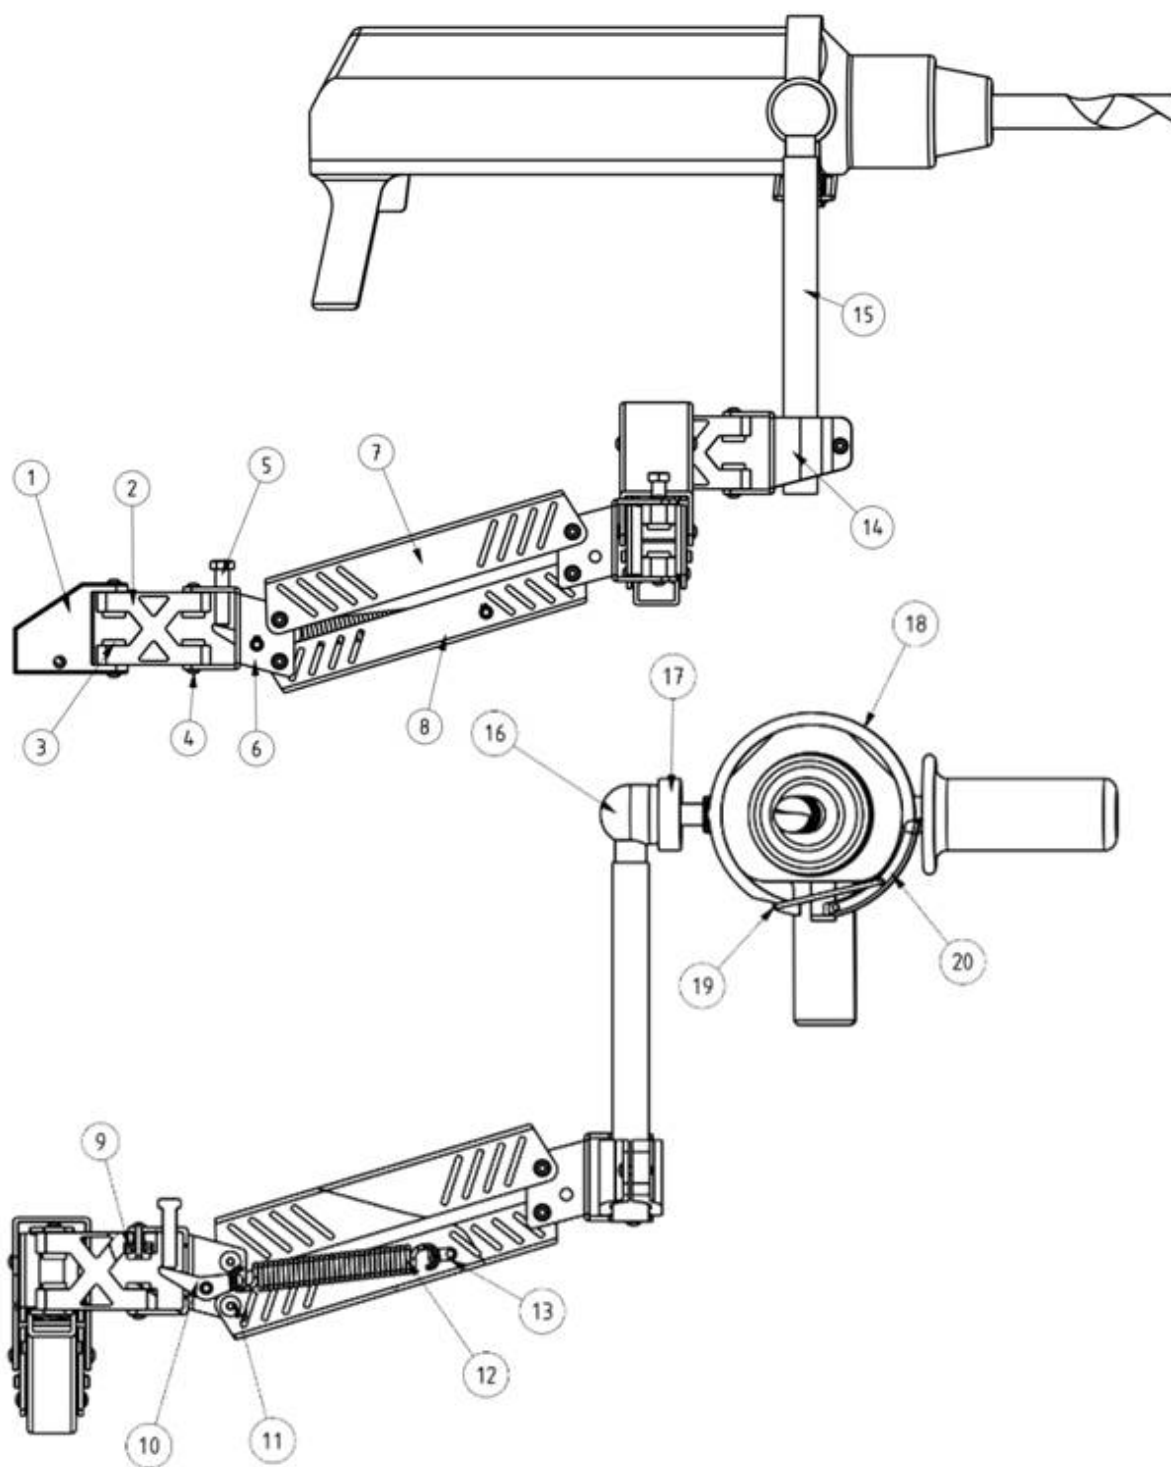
Сборочный чертеж манипулятора экзоскелета.
